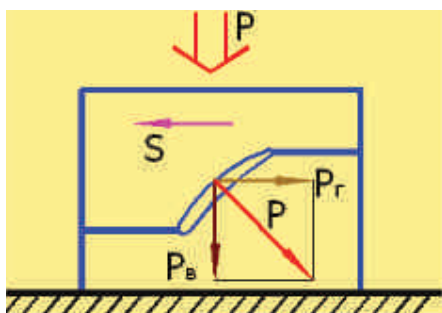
Схема штамповки лопатки с закрученным профилем пера
